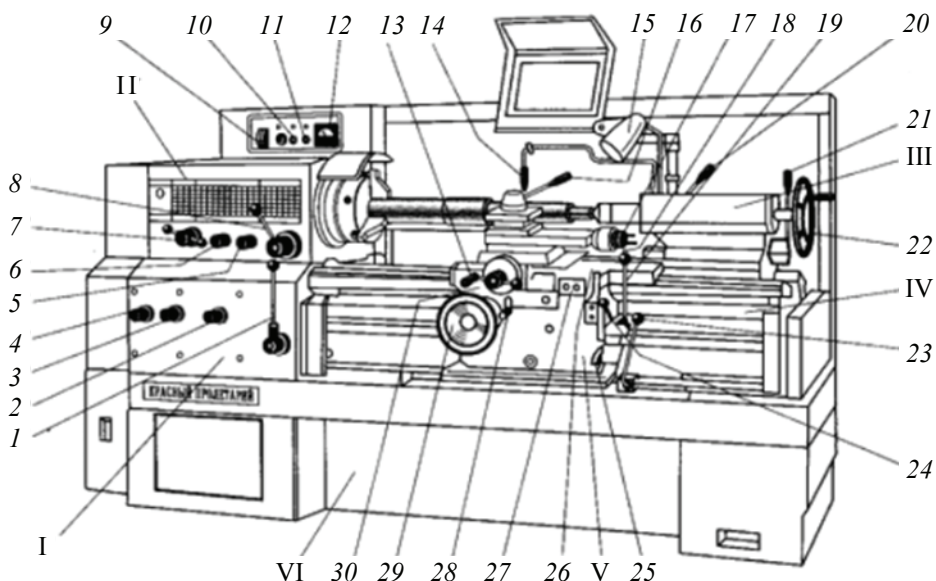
Схема токарно-винторезного станка 16К20 и органов его управления:
